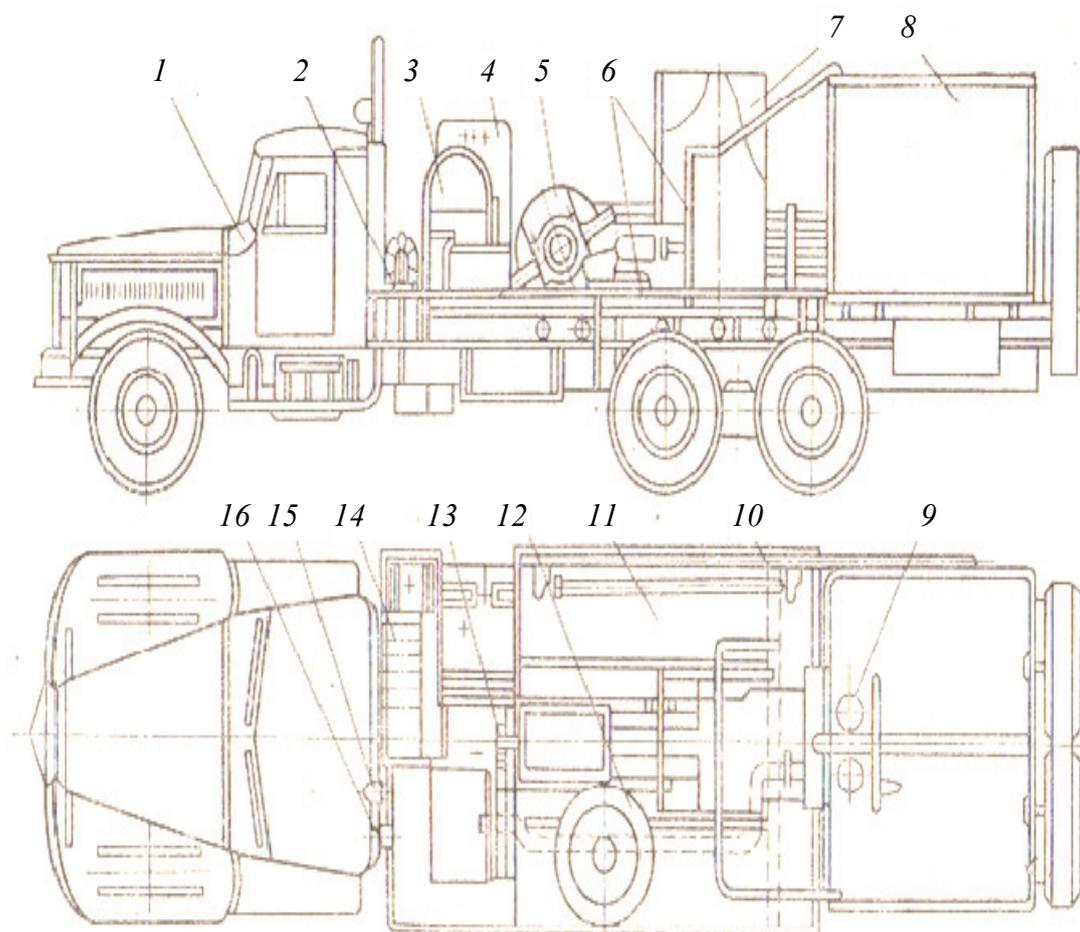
Цементировочный агрегат ЦА-320М: 1 – кабина; 2 – коробка отбора мощности; 3 – насос Ш; 4 – двигатель ГАЗ-51; 5 – двухпоршневой насос 9Т; 6 – обвязка агрегата; 7 – защитный кожух насоса 9Т; 8 – мерный бак; 9 – донные клапаны; 10 – гибкий металлический шланг; 11 – платформа агрегата; 12 – цементомешалка; 13 – карданный вал; 14 – шарнирные колена; 15 – фара и электрооборудование; 16 – выхлопная труба
